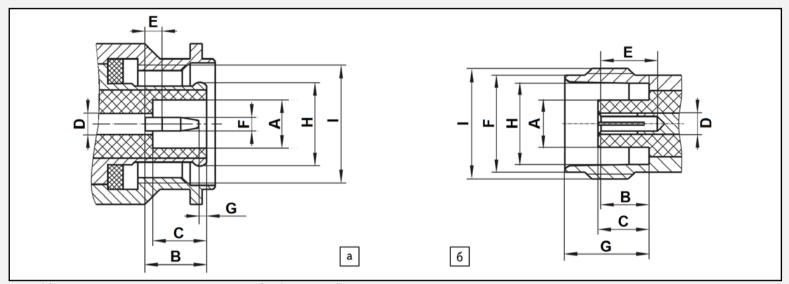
Интерфейс соединителя тип TNC: а) вилка; б) розетка
